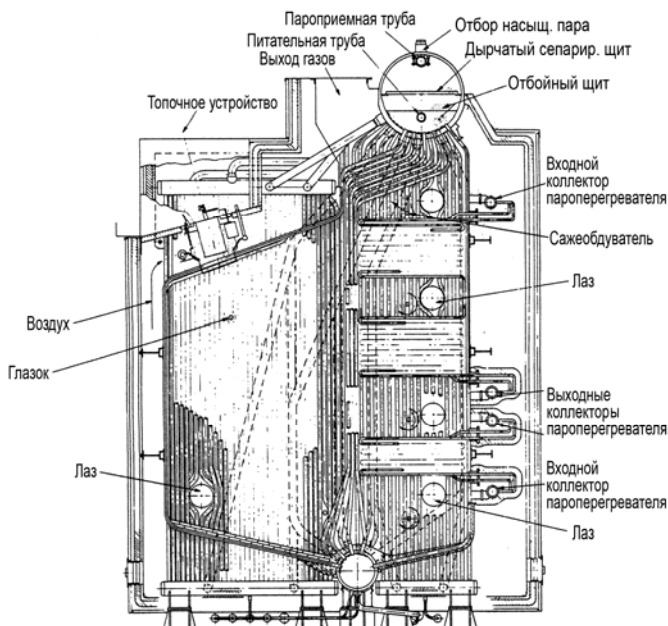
Современный котлоагрегат шахтного типа (U-тупе) газозова
